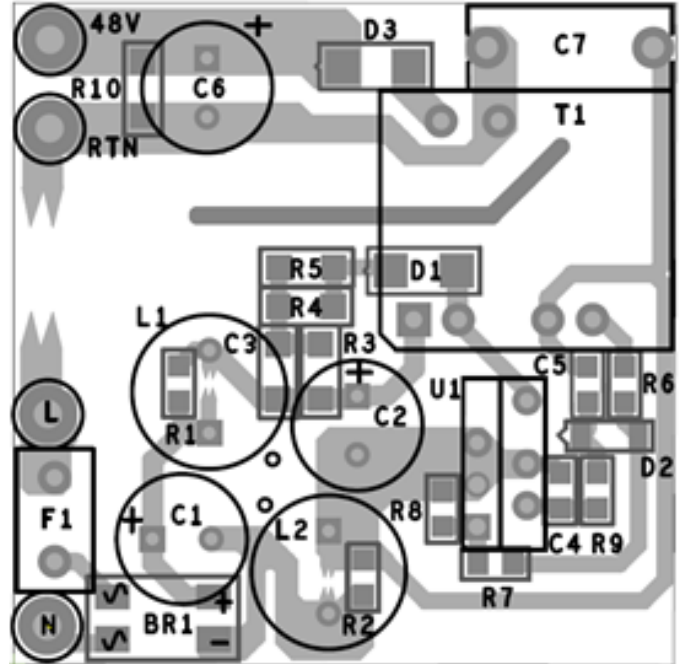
使用 eSIP 封裝的 PCB 佈局範例。
